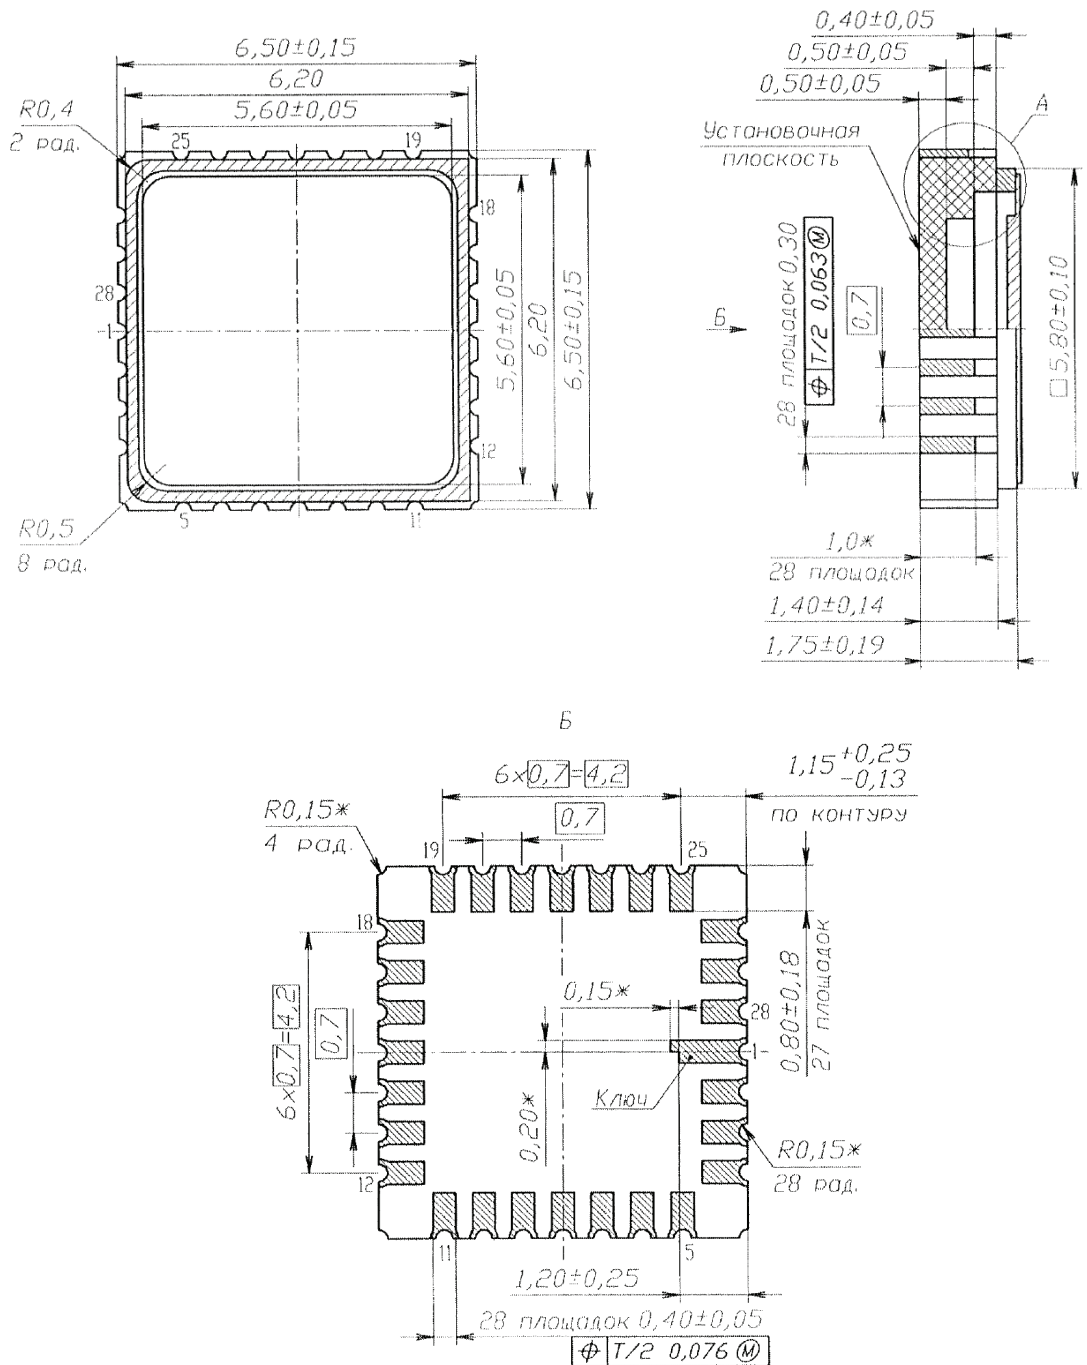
Чертеж корпуса МК 5123.28-1.01
